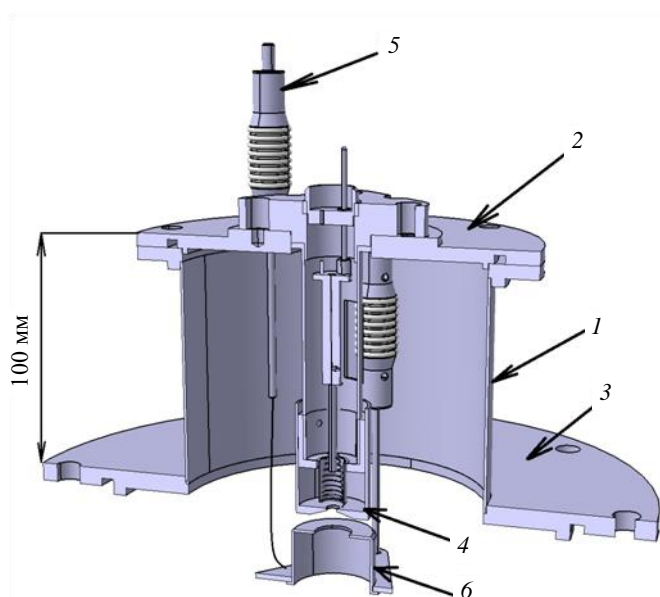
Новая конструкция эмиттерного блока: 1 — корпус эмиттерного блока; 2 — крышка эмиттерного блока; 3 — соединительный фланец; 4 — патрон эмиттера; 5 — подвод экстракторного напряжения; 6 — экстракторный электрод
